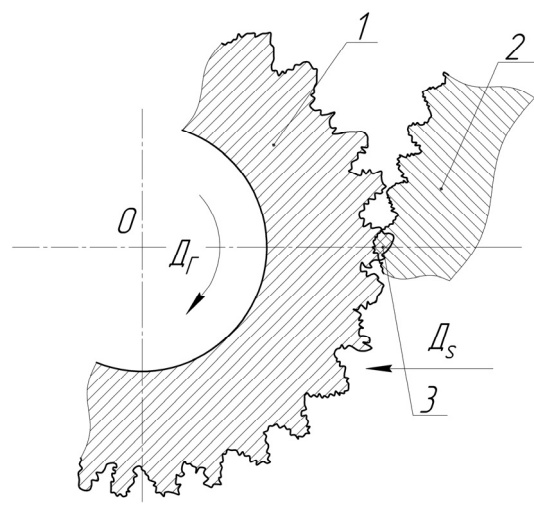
Схема адгезионного износа при скользящем течении: 1 – заготовка; 2 – режущая кромка; 3 – место холодной сварки
